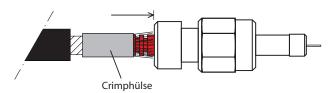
F-SMA Steckverbinder mit Crimphülse und Knickschutztülle
